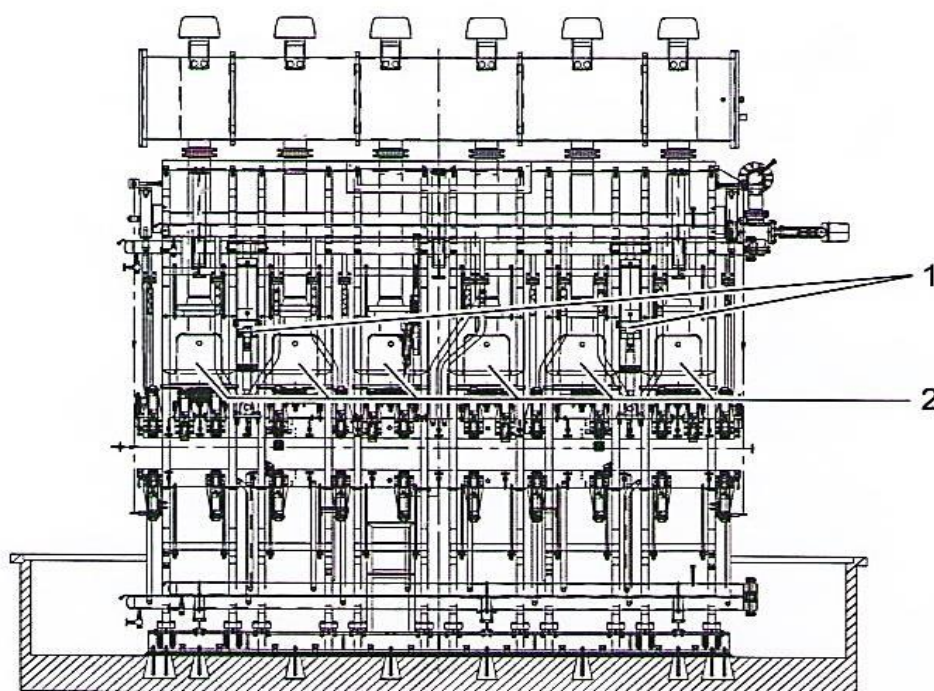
Расположение цилиндров в прессе: 1- главные цилиндры, 2- цилиндры обратного хода
